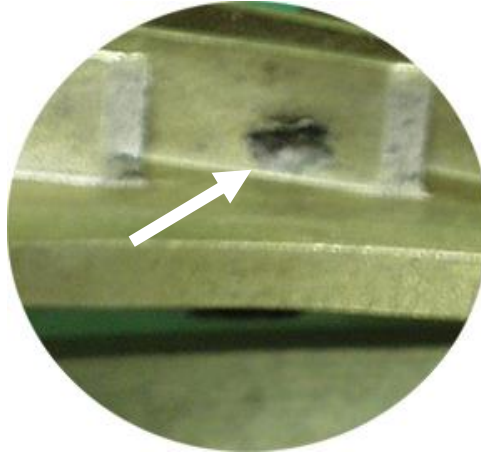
Osady zanieczyszczeń na wirniku turbosprężarki
